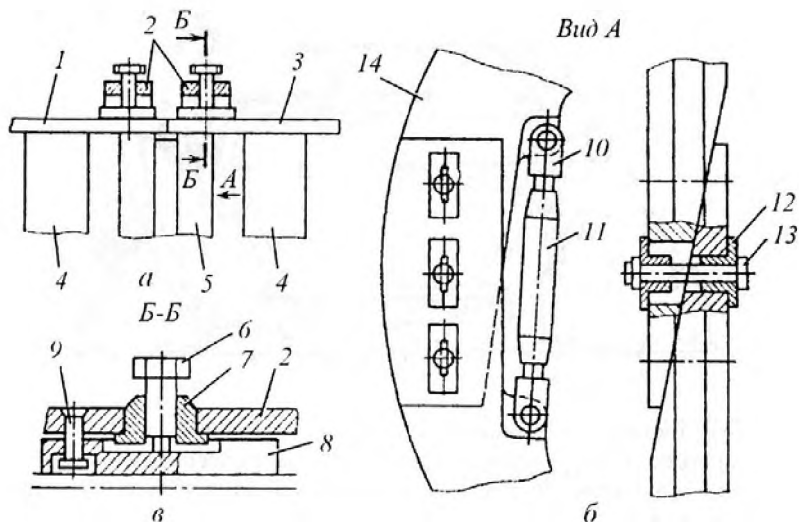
Схема взаимной ориентации деталей при сварке кольцевых швов: а – схема расположения разжимного, калибровочного и бандажного колец; б – конструкция разжимного кольца; в – схема фиксации кромок свариваемых деталей; 1,3 – свариваемые детали; 2 – бандажные кольца; 4 – калибровочные кольца; 5 – разжимное кольцо; 6 – нажимной винт; 7 – втулка; 8 – клавишный прижим; 9 – винт; 10 – резьбовые тяги; 11 – тандер; 12 – втулка; 13 – стяжной болт; 14 – секторы разжимного кольца
